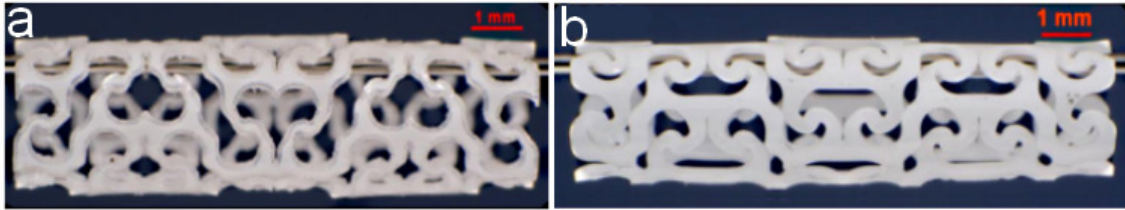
Expandierter Polymerstent (3,0 mm) mit dem Design D63h, gefertigt mit CO₂-Laser (a) bzw. Ti:Sa-Laser (b) aus getauchtem Halbzeug: PLLA/P(4HB) 77,5/22,5 % (w/w), Außendurchmesser: 1,7 mm, Wandstärke: 0,15 mm.
